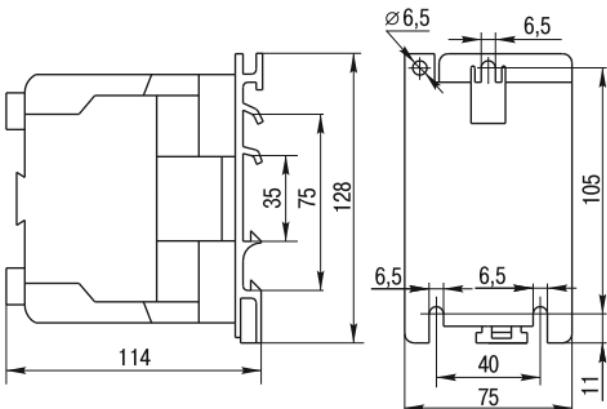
Габаритные и установочные размеры КМИ-48012, КМИ-49512
